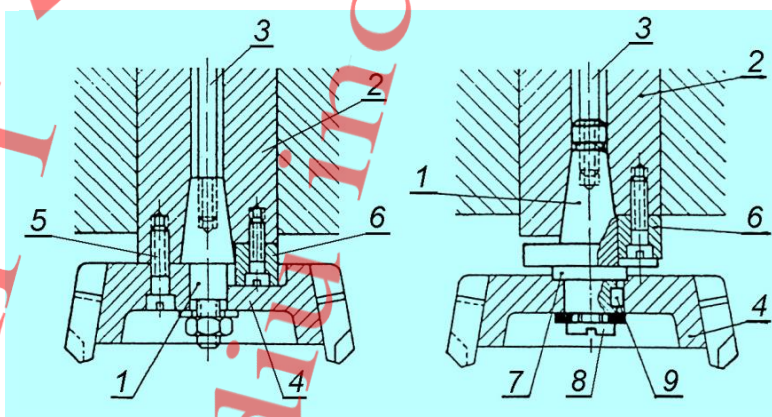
Montarea frezelor frontale cu alezaj pe arborele principal: (a) – fixare directă; (b) – fixare indirectă.
